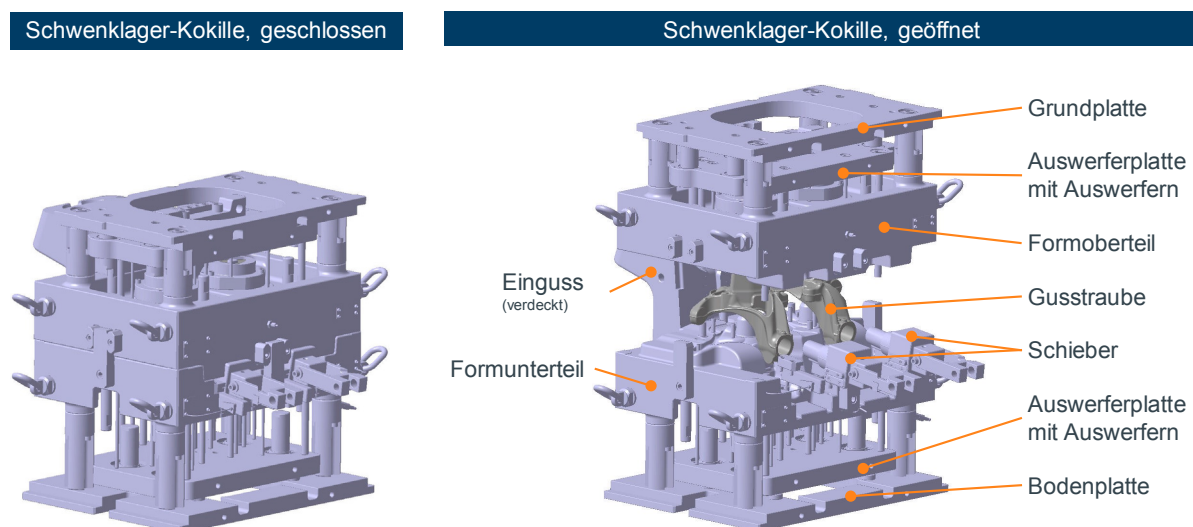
Schwenklager-Kokille für Schwerkraft-Kokillenguss
